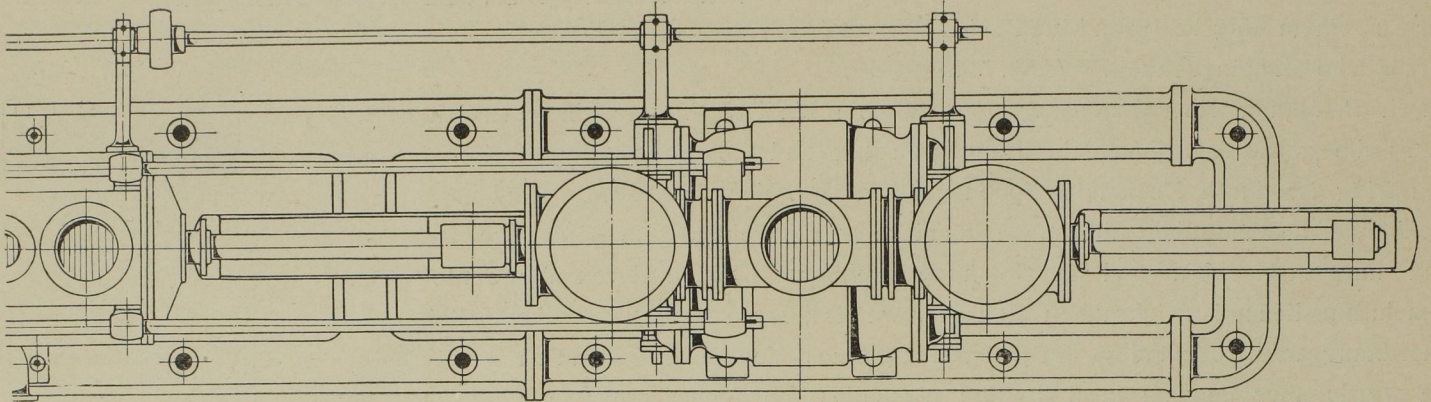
Grundriss des Windcyinders. Masst. 1:50.
